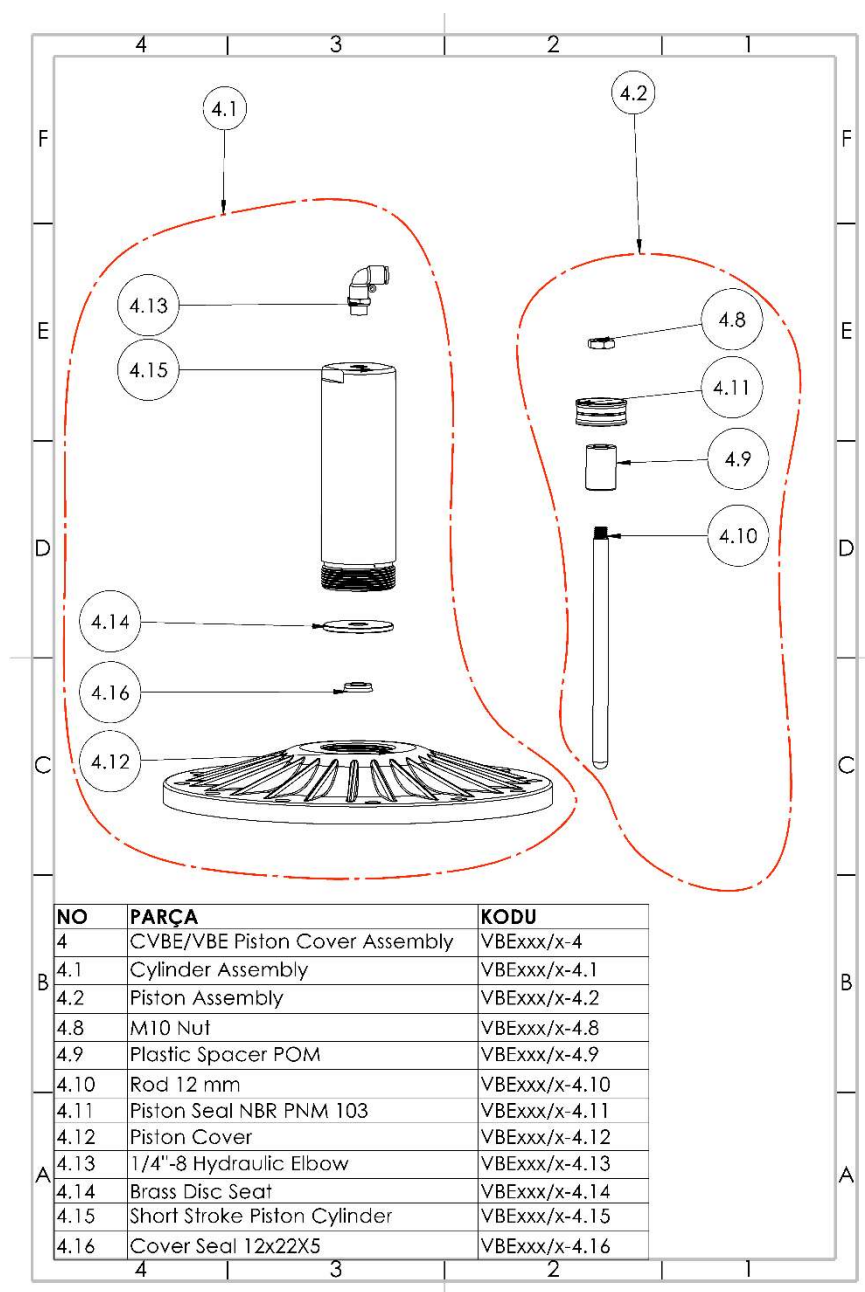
Поршневой комплект крышки серии VBE/CVBE
